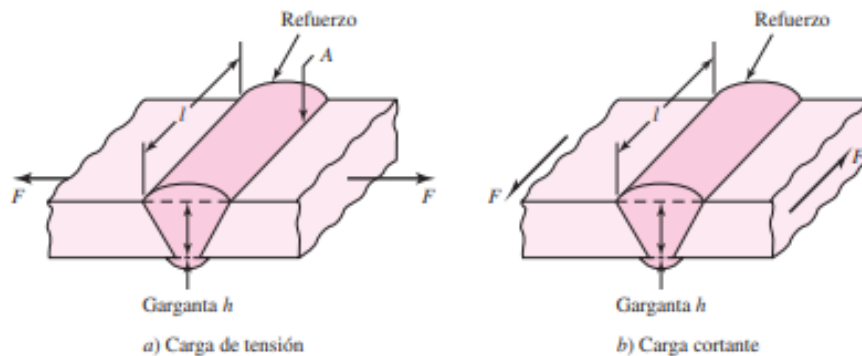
Unión de soldadura con esfuerzos en a) tensión y b) cortante.
